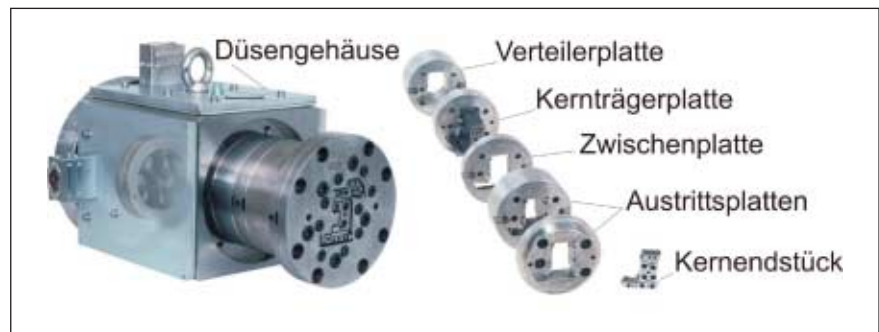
Hohlkammerwerkzeug für ein Rahmenprofil (Quelle: Gruber & Co Extrusionstechnik)
